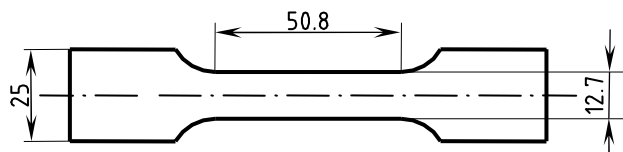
Especimen para ensayo a tracción de chapa (medidas en mm)
